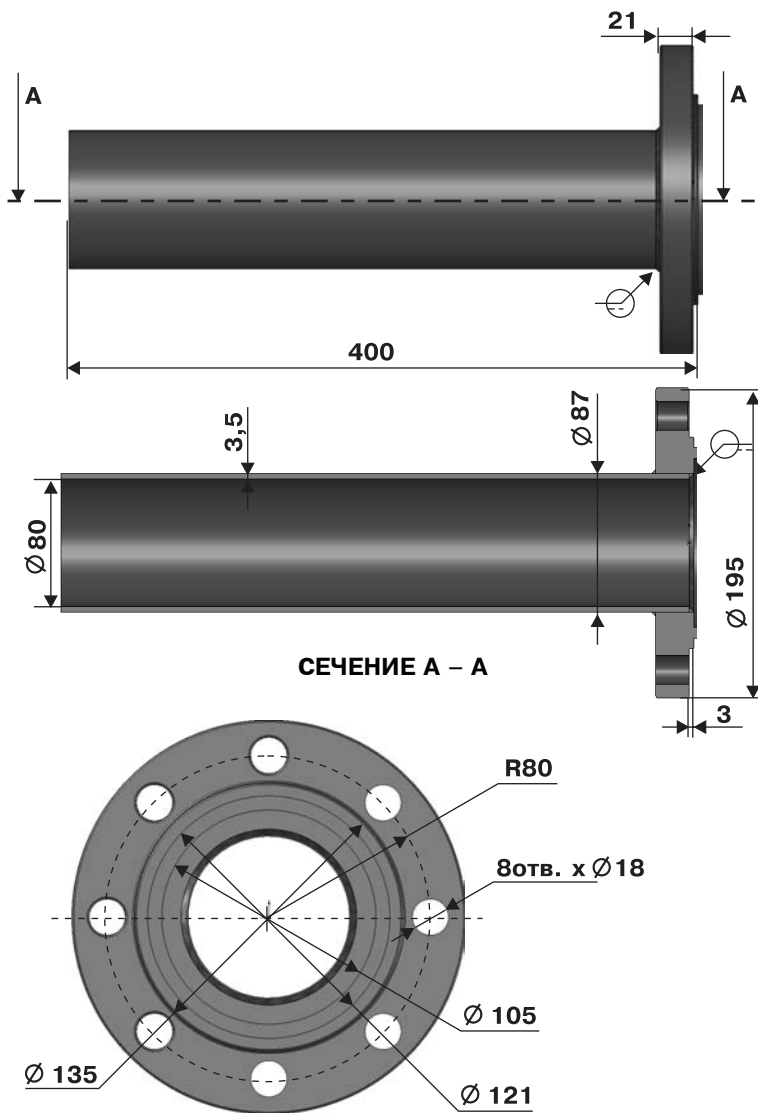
Габаритные и установочные размеры КМЧ 3 ДУ80
